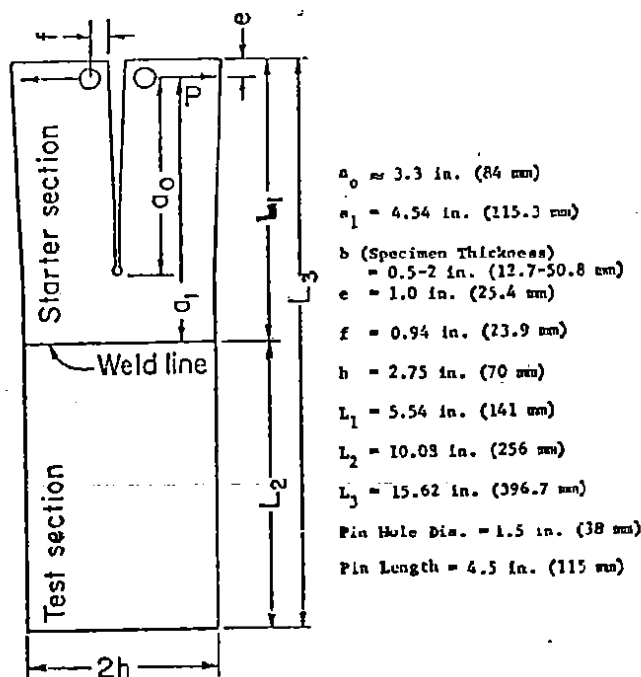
Géométrie et dimensions de l'éprouvette DCB (Hahn et al., 1976)
